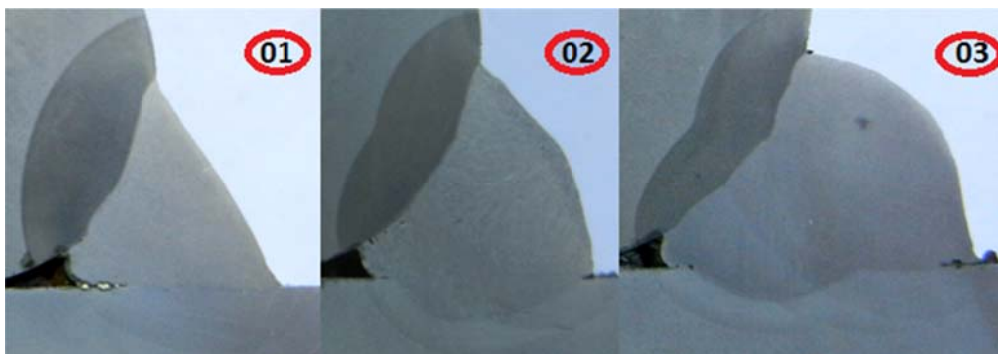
Macrografia dos corpos de prova soldados com pré-aquecimento e sem pós-aquecimento. (01) Um cordão de solda, (02) dois cordões de solda e (03) três cordões de solda.
